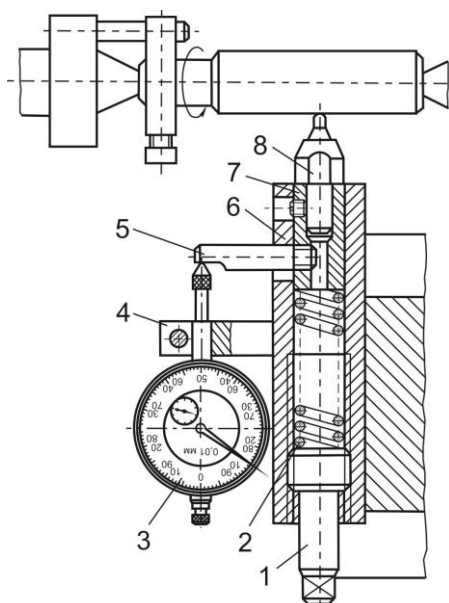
Державка пружинного типа: 1 – регулировочный винт, 2 – тарировочная пружина, 3 – индикатор часового типа, 4 – державка, 5 – упор, 6 – корпус, 7 – шток, 8 – алмазный выглаживатель
